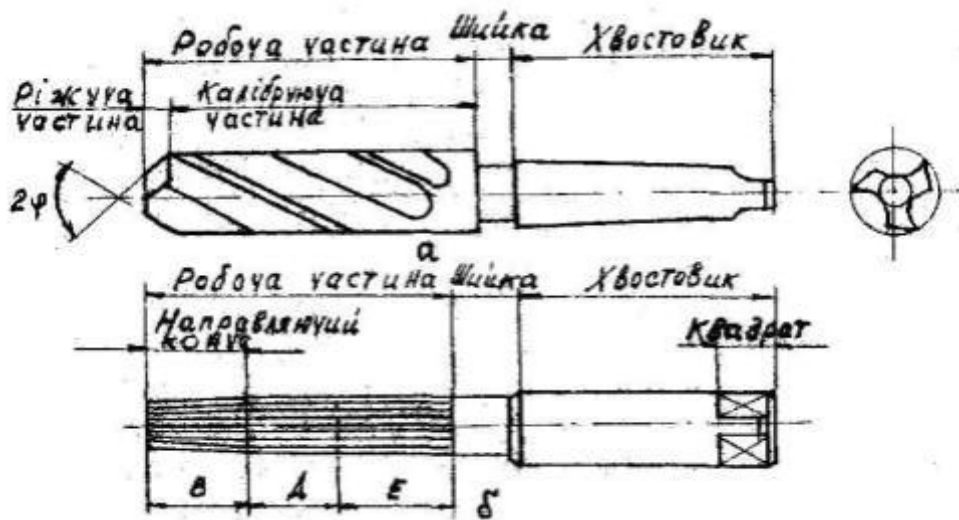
Циліндричний зенкер /а/ та розвертка /б/
